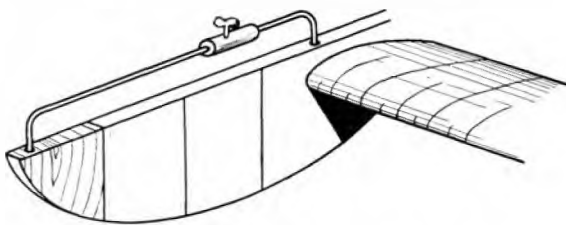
Unzweckmäßige Trimmgewichtbefestigung.
